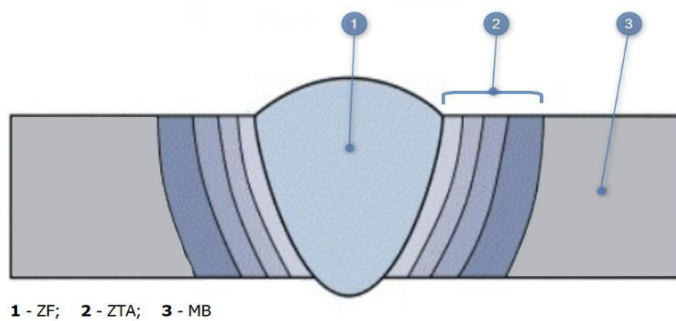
Ilustração das três principais zonas de uma junta soldada
